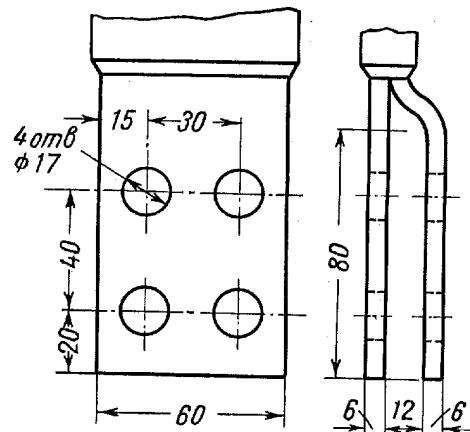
Размеры выводных пластин обмотки статора электродвигателя типа SM-12000-2
